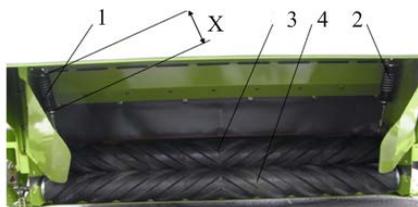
Настройка натяжения валцов плющилки: 1, 2 – пружины; 3 – верхний валец; 4 – нижний валец
